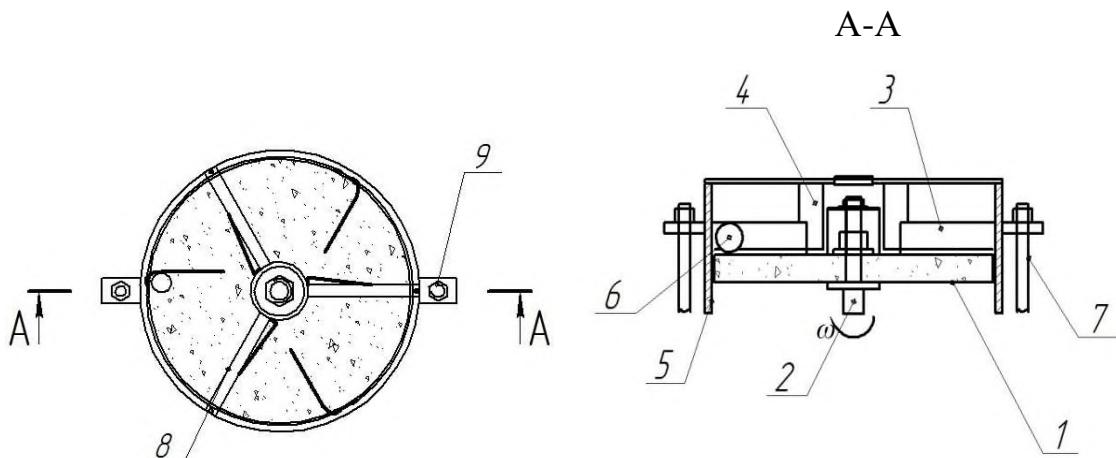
Устройство для обработки шариков из самоцветных камней
